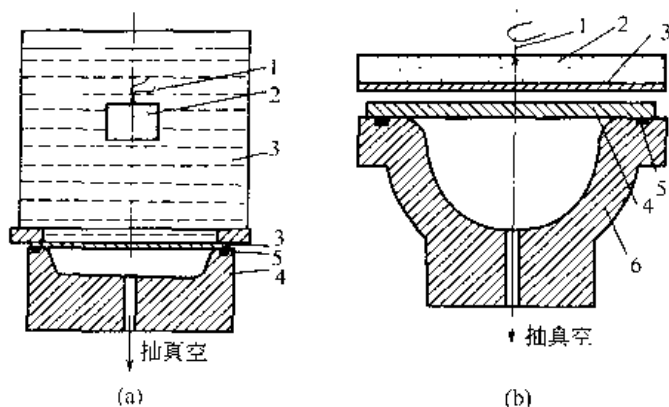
爆炸焊接-爆炸成形工艺示意
